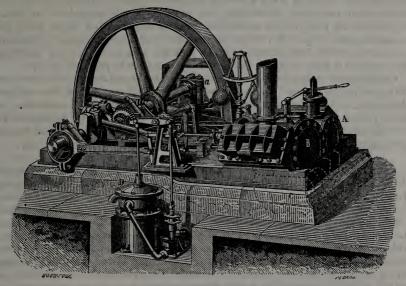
Machine à cylindre de M. May, de Birmingham.
